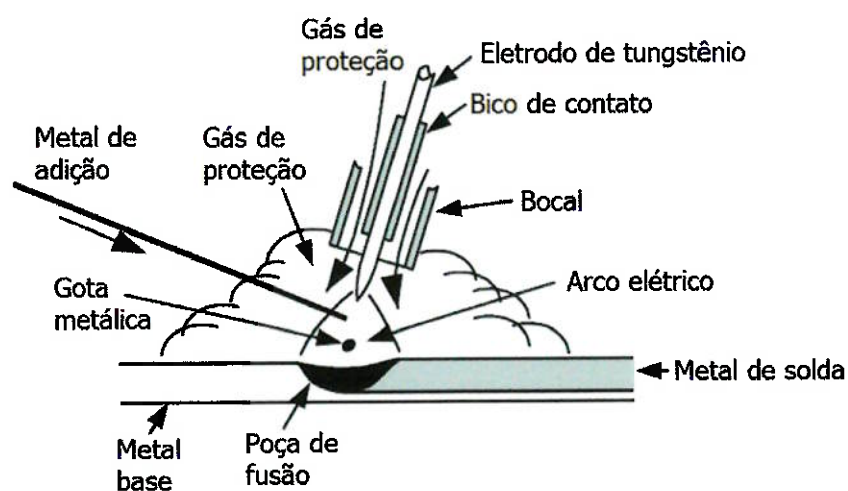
Processo de soldagem ao arco com eletrodo de tungstênio [7, adaptado]
